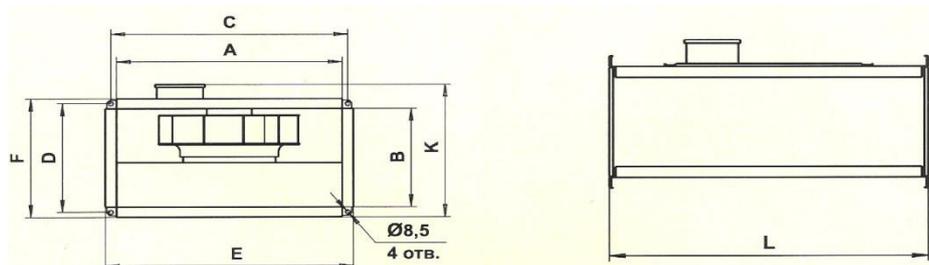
Устройство канального вентилятора ВК 30-15
